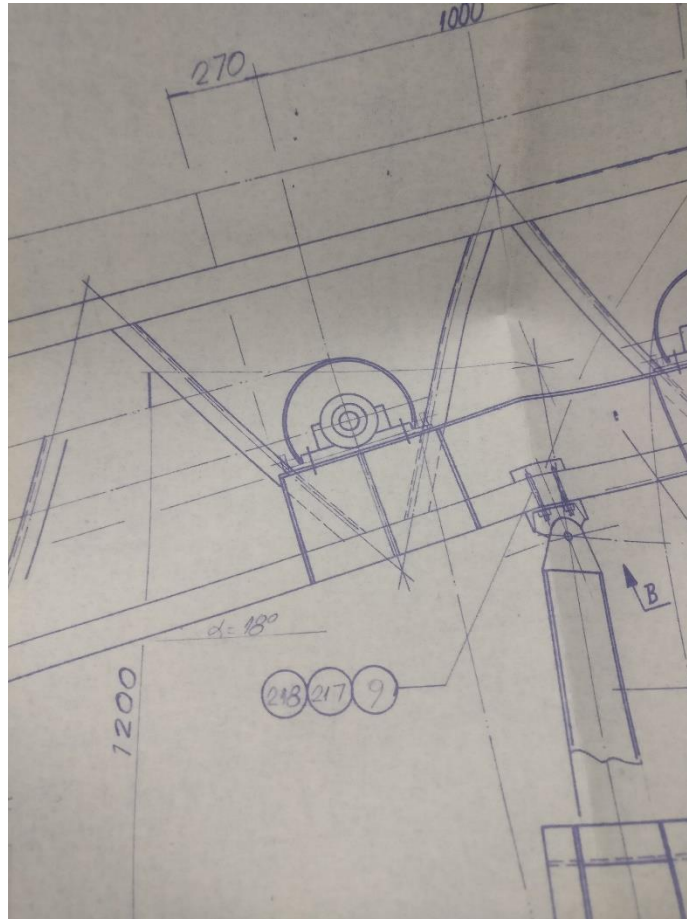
Posição do tambor de dobra no desenho técnico (arquivo pessoal).
